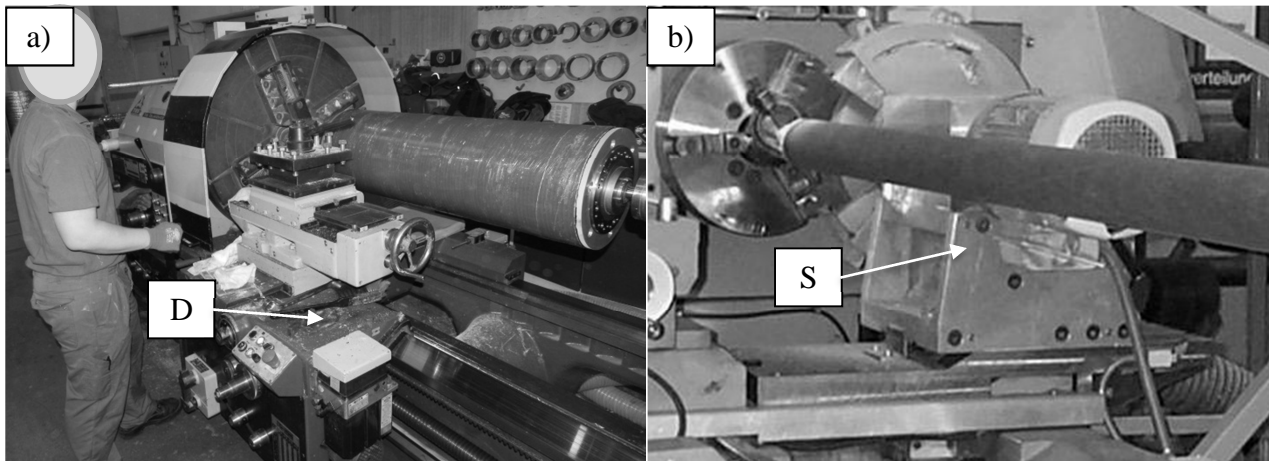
Oberflächenbearbeitung [TMa 11], a) Drehmaschine mit DTS , b) Schleifspindel mit Halter im Einsatz
